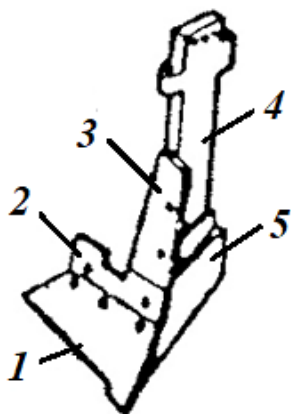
Змінний безвідвальний корпус-розпушувач:
